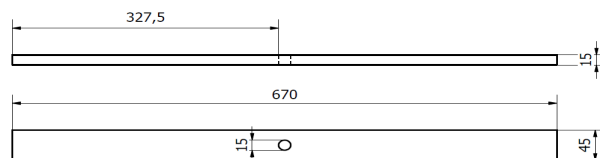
Esquema de la geometría de las probetas con agujero (cotas en mm).
